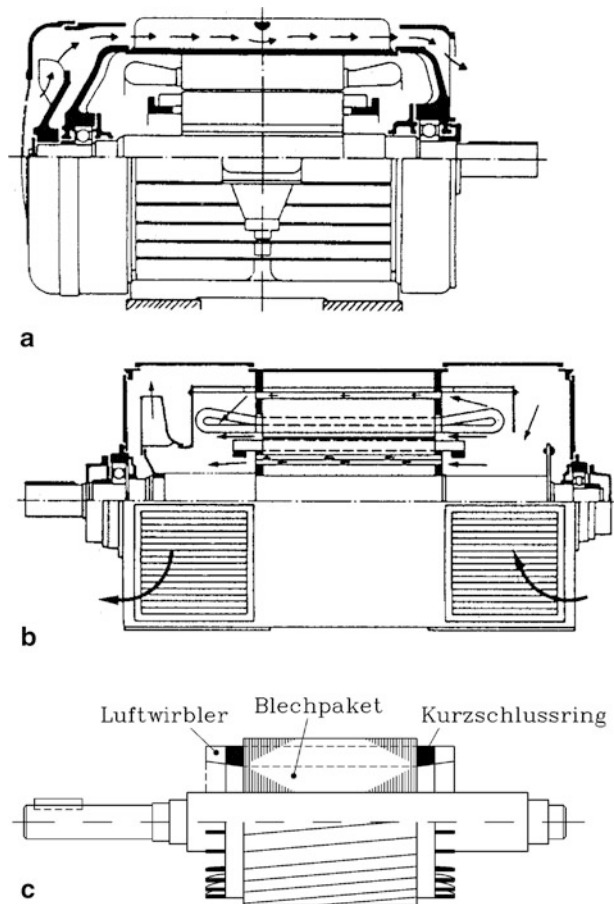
Käfigläufer-Asynchronmaschinen: (a) Oberflächegekühlte Niederspannungs-Asynchronmaschine als IEC-Normmotor mit Einschicht-Runddraht-Wicklung im Ständer und Rippengehäuse, Aluminium-Druckguss-Käfig im Läufer und Wellenlüfter, (b) Innenbelüftete Käfigläufer-Asynchronmaschine mit Hochspannungs-Zweischichtwicklung im Ständer, hart gelötetem Kupfer-Käfig im Läufer und Radial-Wellenlüfter, axiale Kühlluftführung durch den Luftspalt und axiale Ständer- und Läuferkühlkanäle (Quelle: Bohn 1987), (c) Aluminium-Druckguss-Käfigläufer mit geschrägten Stäben zur Verringerung des Nutungseinflusses auf das Drehmoment, angegossene „Lüfterflügel“ als Luftwirbler an den Kurzschluss-Ringen zur verbesserten Wärmeabfuhr aus dem Läuferkäfig (Quelle: Kleinrath 1975)
